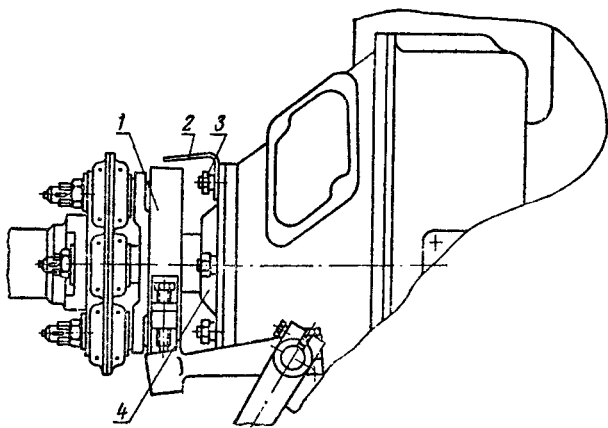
Установка стрелки для проверки угла опережения подачи топлива:
